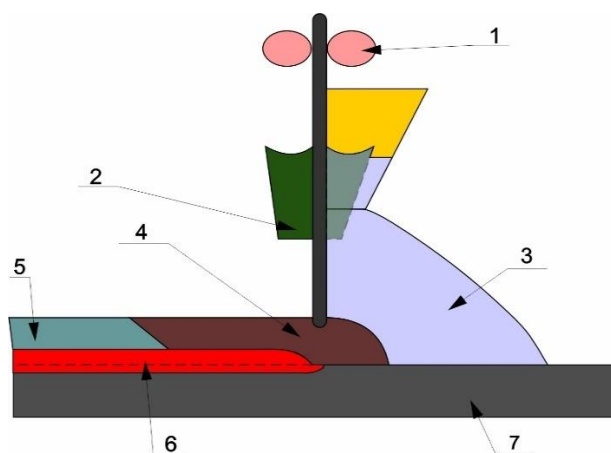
Схема процесу електрошлакового наплавлення однією електродною стрічкою: 1 – стрічкоподавальний механізм; 2 – водоохолоджуваний механізм з тугоплавкими губками; 3 – флюс; 4 – рідкий шлак; 5 – затверділий шлак; 6 – наплавлений метал; 7 – основний метал
